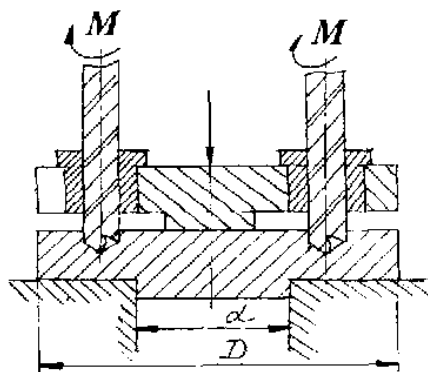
Затиск заготовки кондукторною плитою при свердлінні
